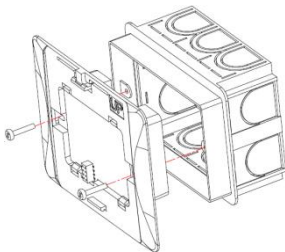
Collegamento placchetta di fissaggio a scatola 503.
